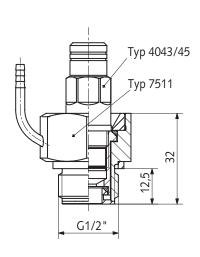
Einbau des Sensor Typs 4045A... in gedämpften Kühladapter Typ 7511
